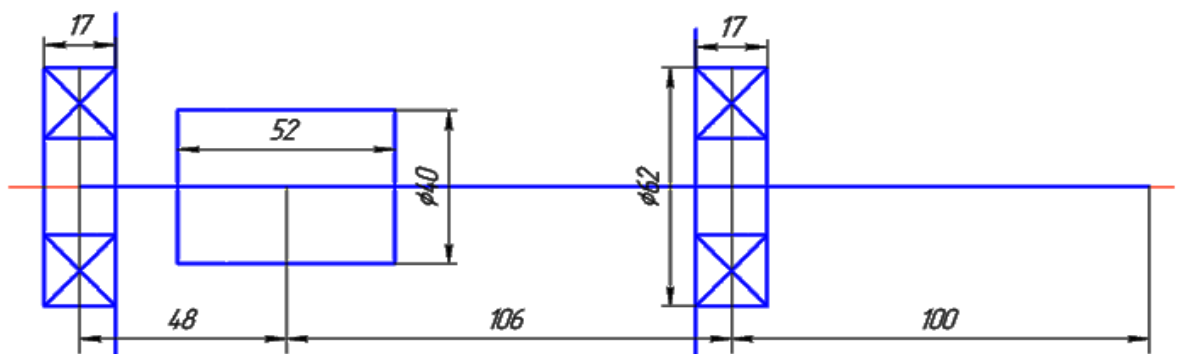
Фрагмент компоновки редуктора (ведущий вал).
